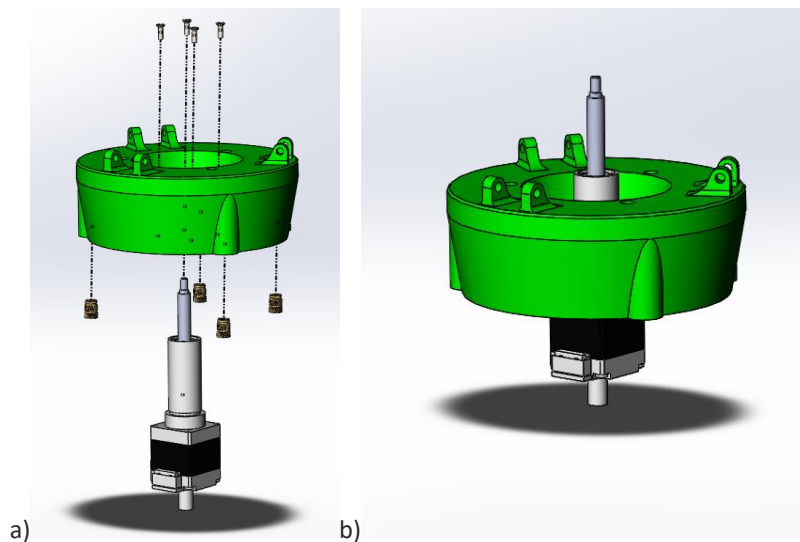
2ª parte da montagem - vista explodida da montagem (a) e parte da montagem completa (b).
